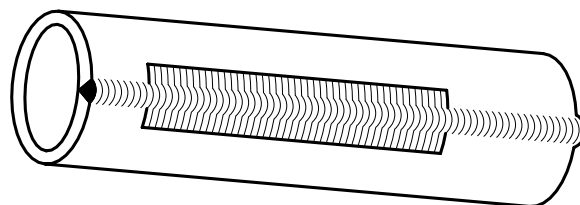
Éprouvette pour essai de la soudure longitudinale des tubes soudés
